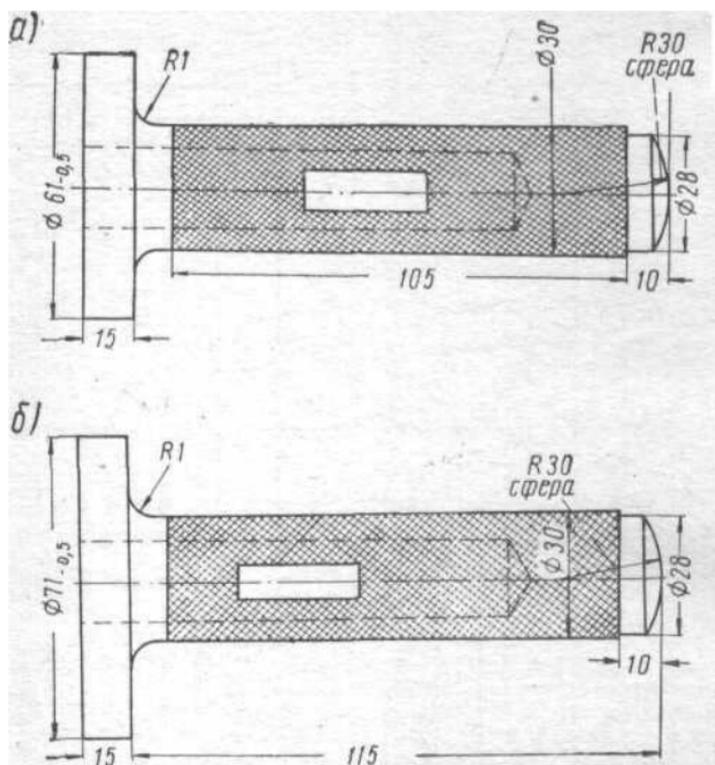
Оправки для запрессовывания наружных колец подшипников вала ведущей шестерни главной передачи:
